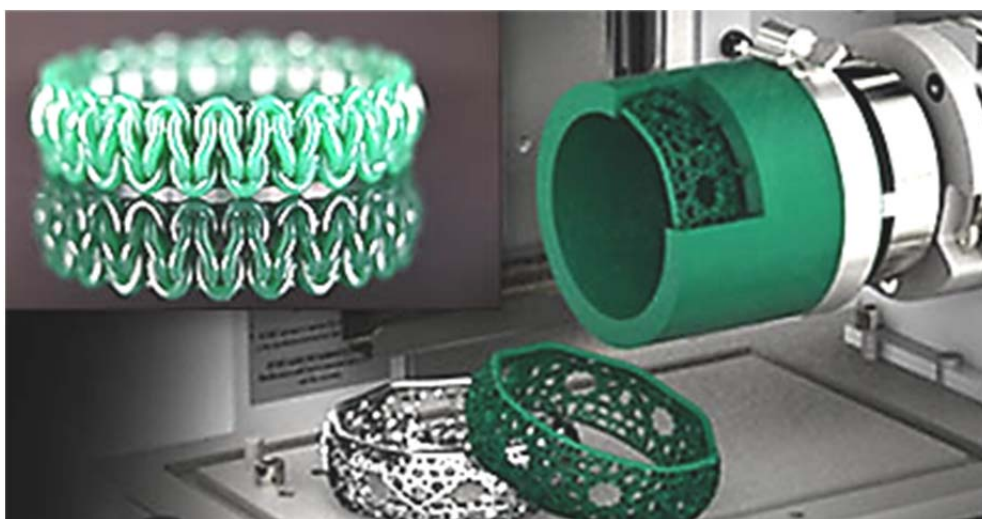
Фрагмент гравірувально-фрезерного верстата з ЧПУ Revo540CX
